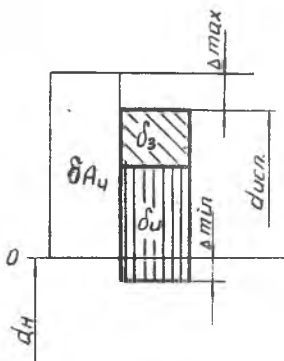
Схема расположения мм. полей допусков при определении исполнительных размеров зенкера
